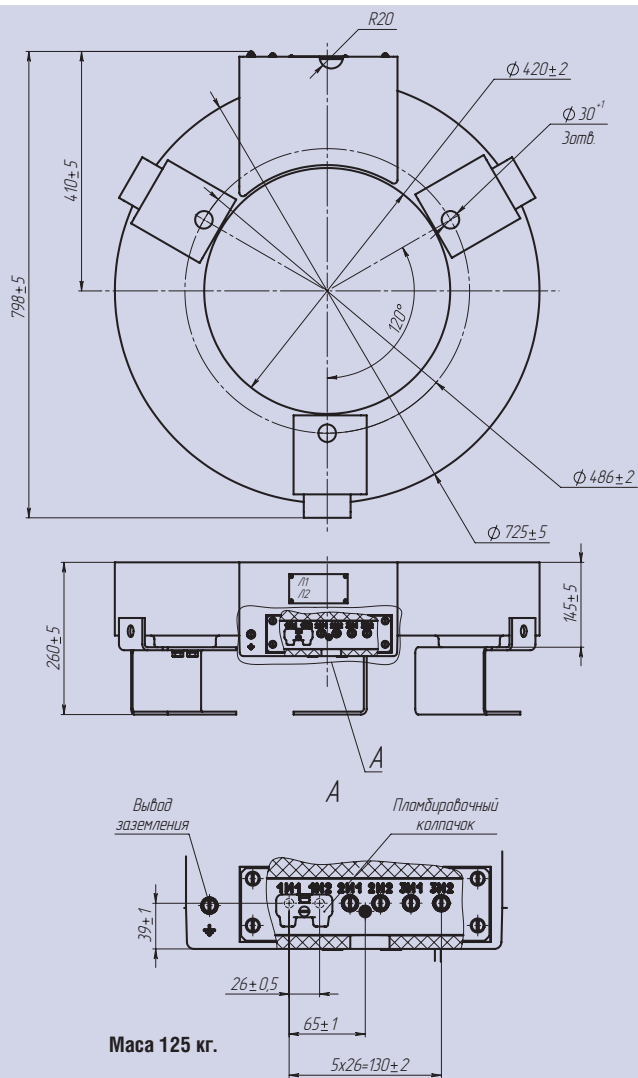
Габаритные, установочные и присоединительные размеры трансформатора ТВ-110-IX-3.
